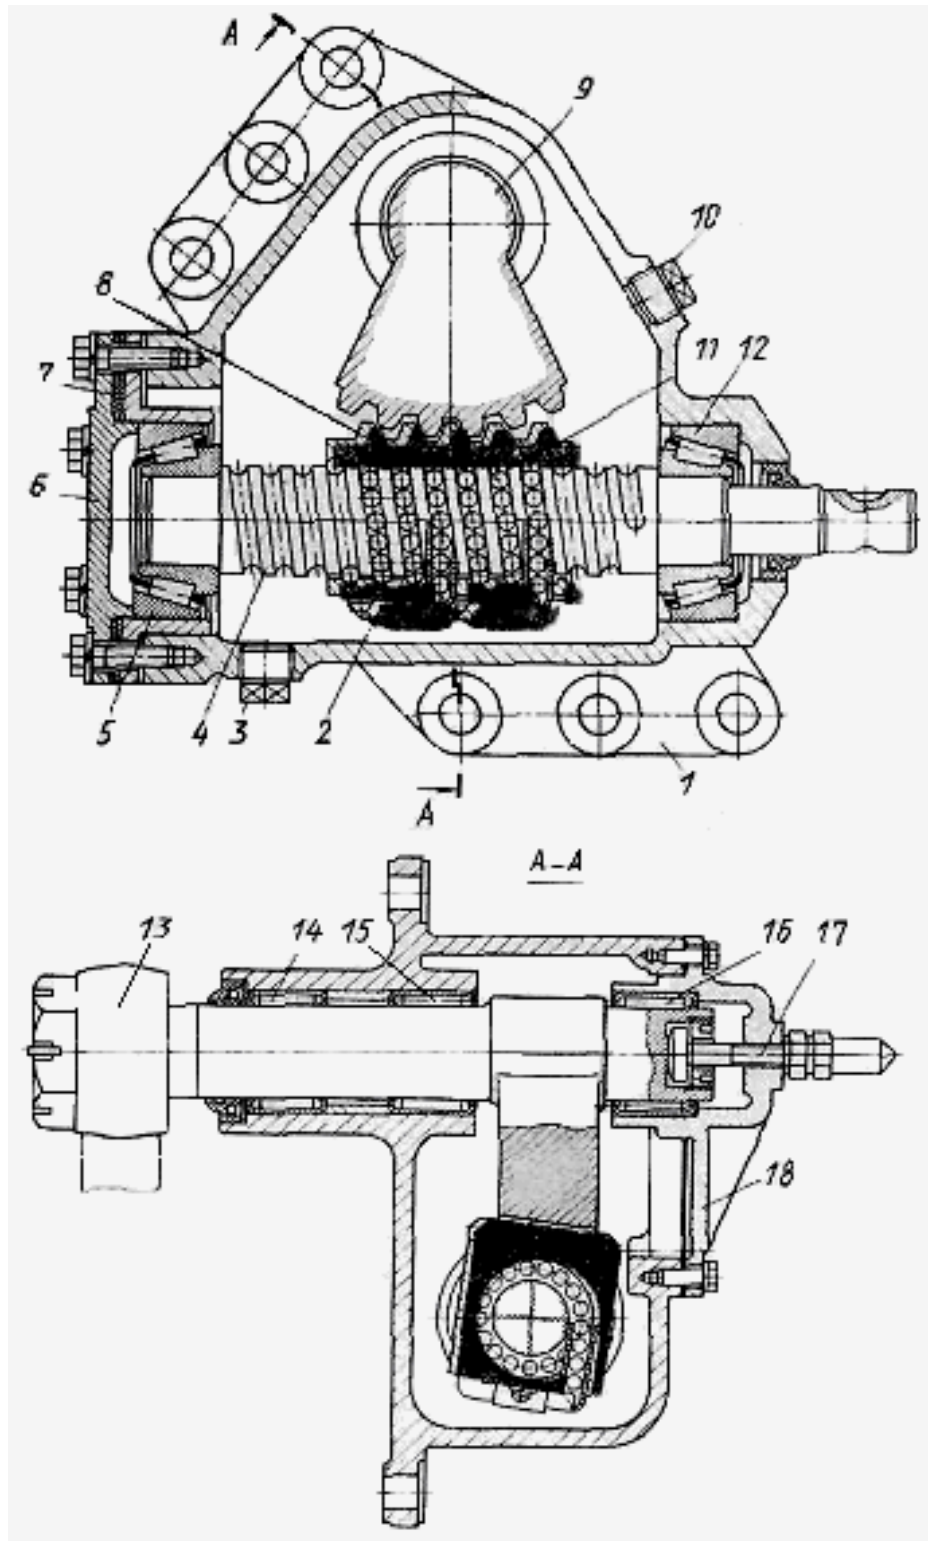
Рулевой механизм автомобиля Белаз-540: 1 - картер; 2 - направляющая трубка; 3 - пробка сливного отверстия; 4 - винт; 5 и 12 - конические роликовые подшипники; 6 и 18 - крышки; 7 - регулировочные прокладки; 8 - гайка с рейкой; 9 - сектор; 10 - пробка заливного отверстия; 11 - шарики; 13 - сошка; 14 и 16 - игольчатые подшипники; 17 - регулировочный винт
